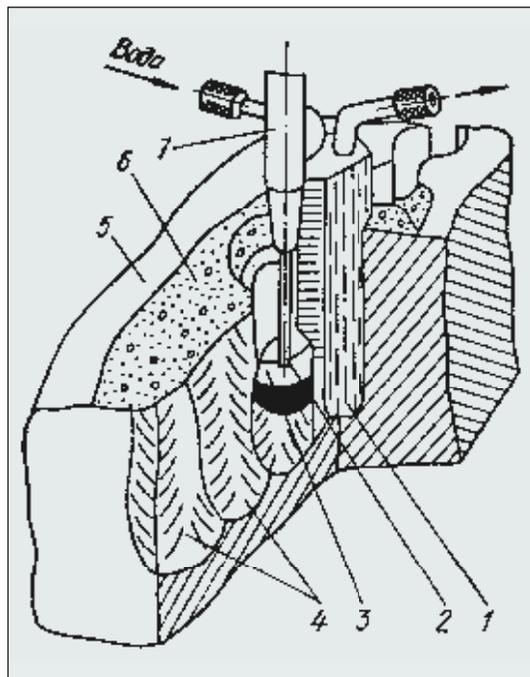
Схема заварки разделки: 1 — формирующее устройство; 2 — электрод; 3 — шлаковая ванна; 4 — шов; 5 — основной металл; 6 — слой флюса; 7 — мундштук
